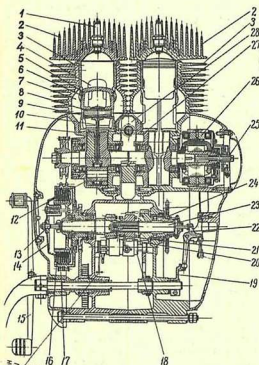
Двигатель с коробкой передач в разрезе: 1 — свеча зажигания; 2 — головка цилиндра; 3 — цилиндр; 4 — выпускное окно; 5 — поршень; 6 — поршневой канал; 8 — поршневой палец; 9 — втулка верхней головки шатуна; 10 — шатун; 11 — крышка кривошипной камеры; 12 — палец кривошипа; 13 — регулировочный винт сцепления; 14 — маятниковый диск сцепления; 15 — педаль переключения передач; 16 — диски сцепления; 17 — наружный барабан сцепления; 18 — вал переключения передач; 19 — кулачок автомата сцепления; 20, 21 — шестерни коробки передач; 22 — рычаг выжима сцепления; 23 — ведущий вал; 24 — ведомый вал; 25 — кулачок прерывателя; 26 — генератор; 27 — крышка кривошипной камеры; 28 — маховик.
